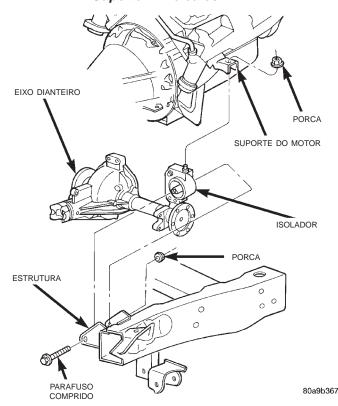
Isolador de Montagem do Motor no Suporte — Veículos 4WD
